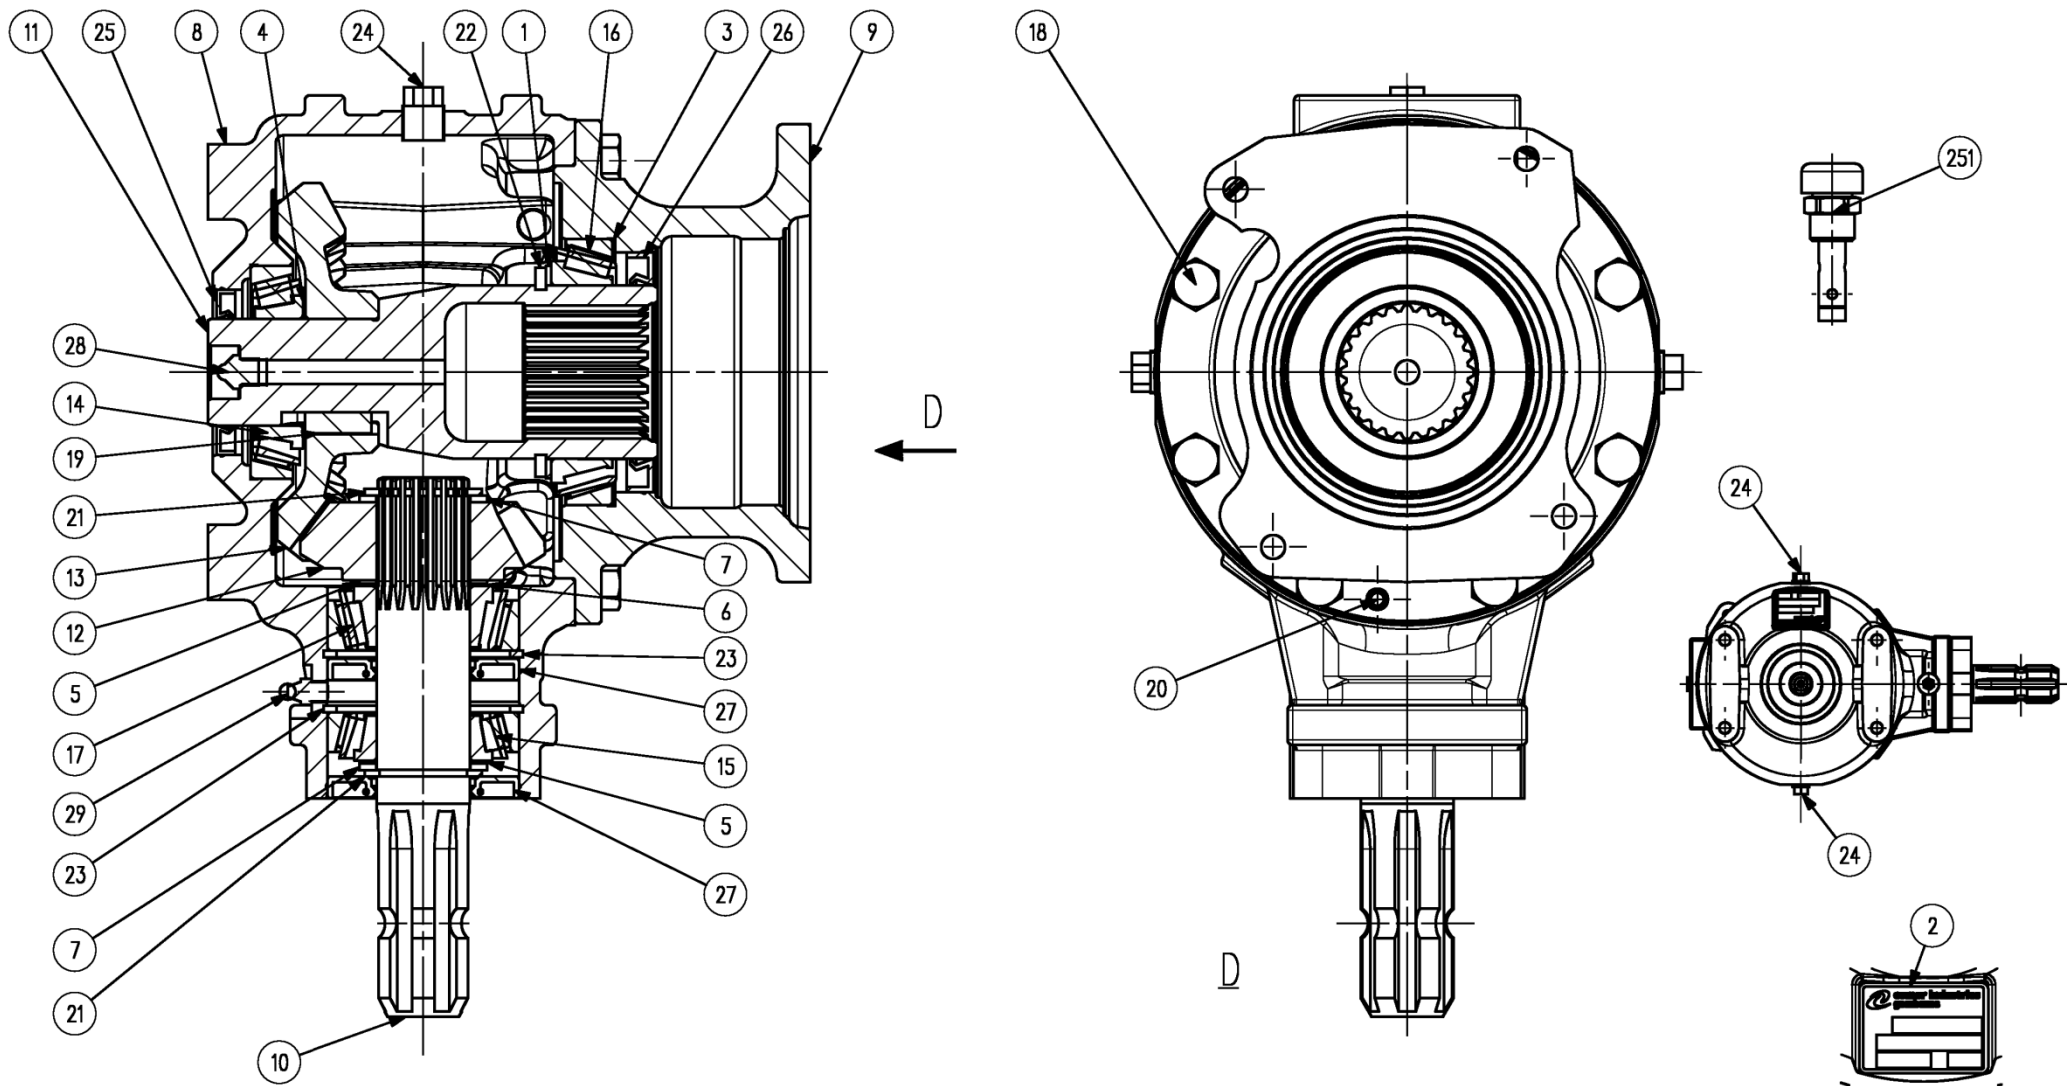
Редуктор 9.304.529.20 (9.304.529.10) "Comer industries"
